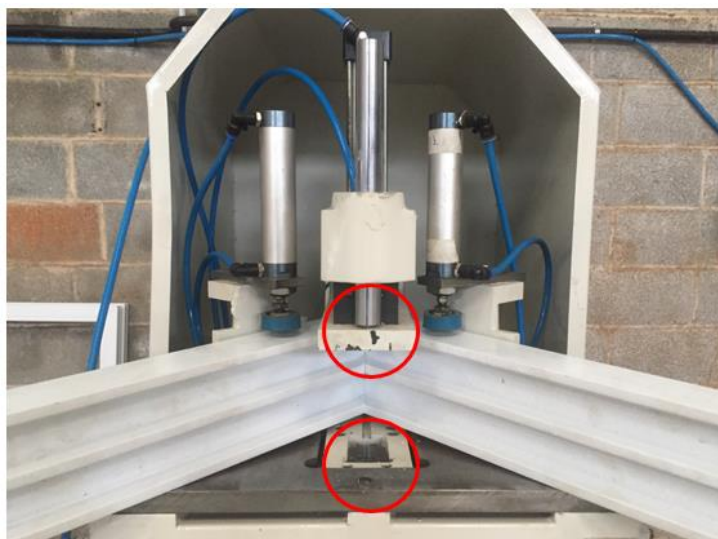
Máquina Rebarbadeira (ou Limpadora de Solda).
